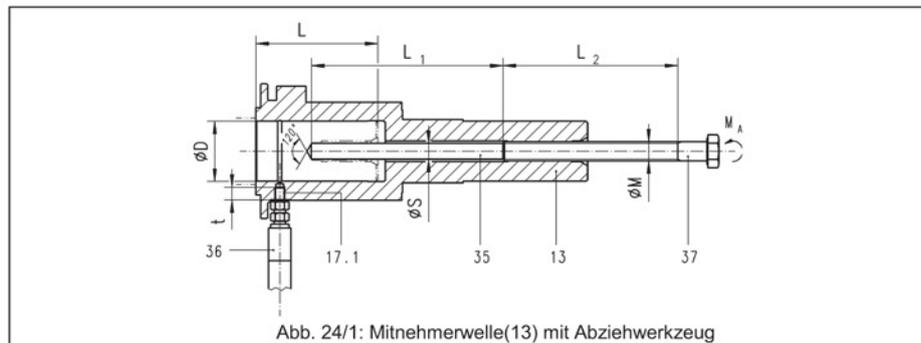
/1: Mitnehmerwelle(13) mit Abziehwerkzeug
